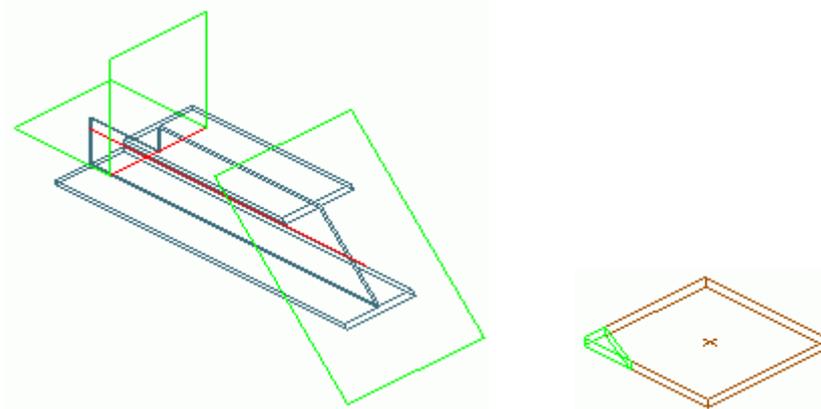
Bearbeitungskonturen Ausklinkung und Eckabschnitt
